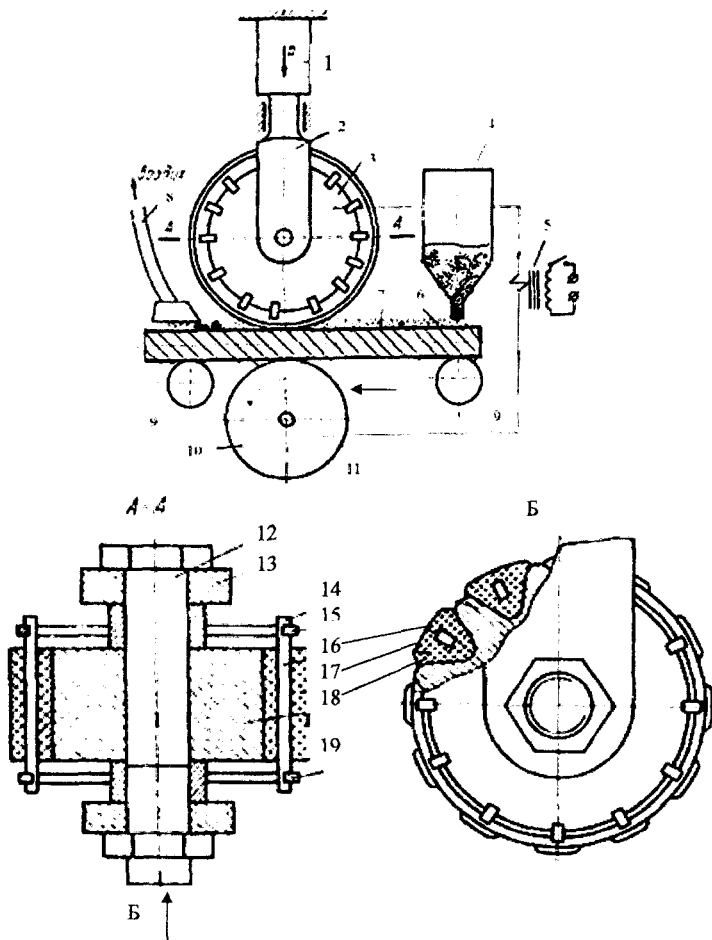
Устройство для нанесения покрытий на зубья цилиндрических зубчатых колес
